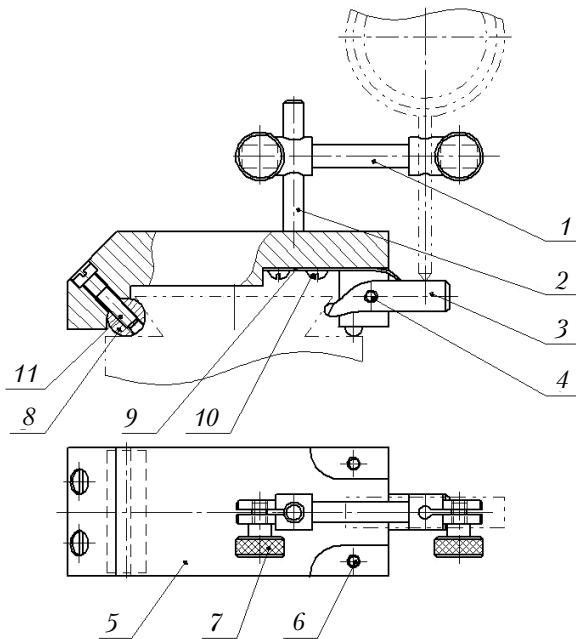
Эскиз приспособления для контроля отклонения от параллельности поверхностей ласточкиного хвоста стола фрезерного станка
